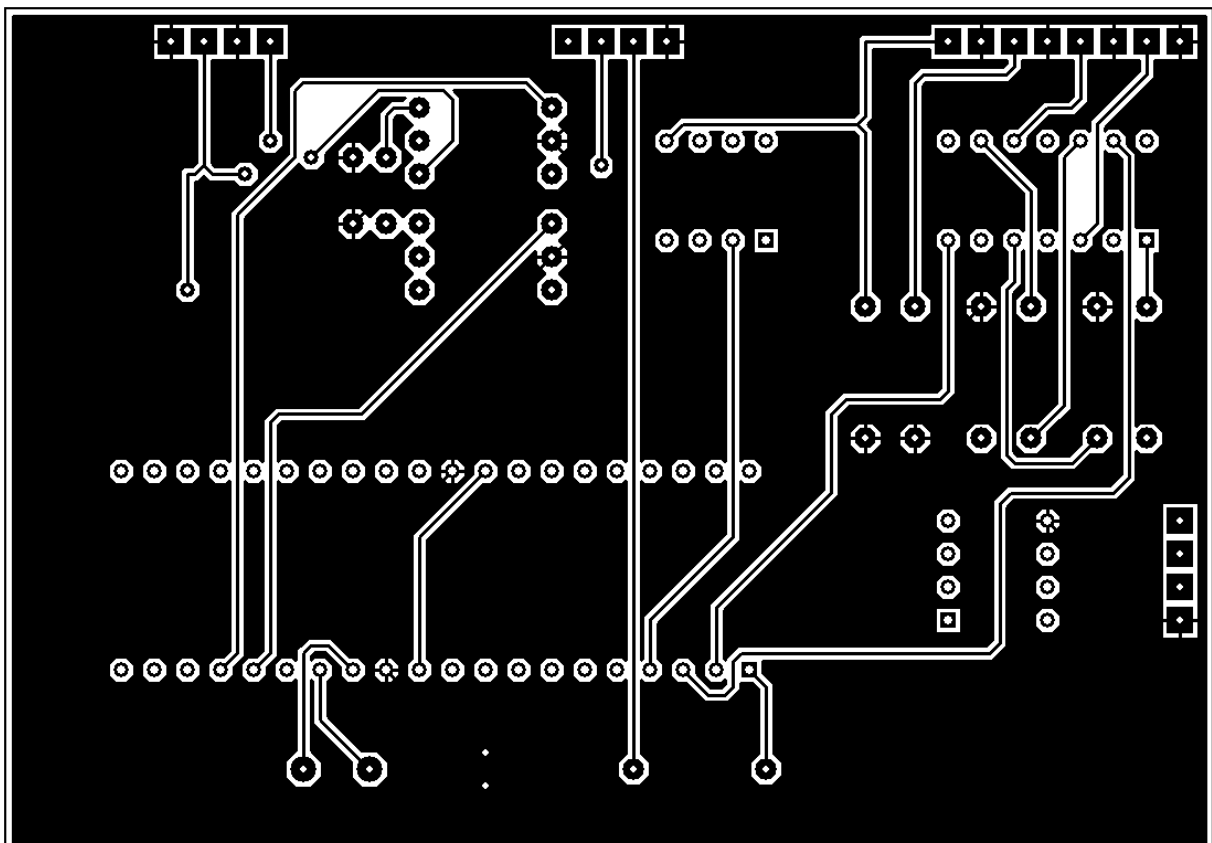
Fotolito PCB fuente de alimentación. Cara inferior
